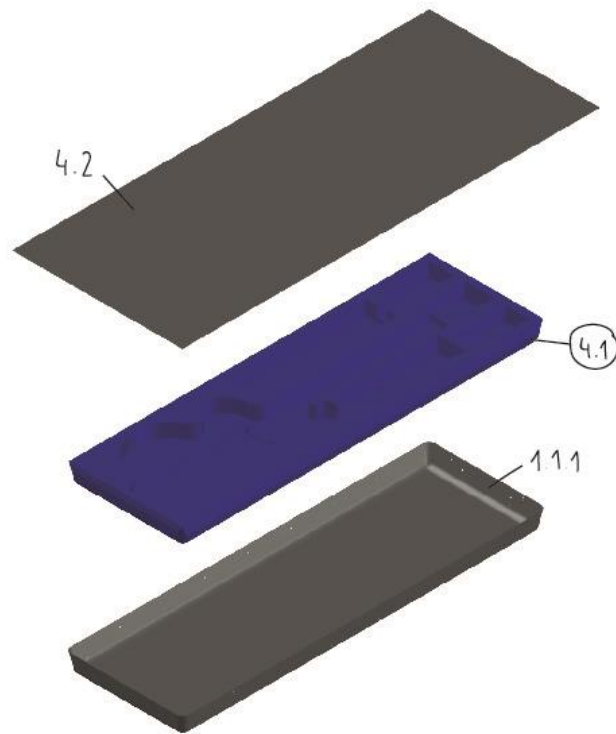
Explosionado de relaciones pieza 4.1
